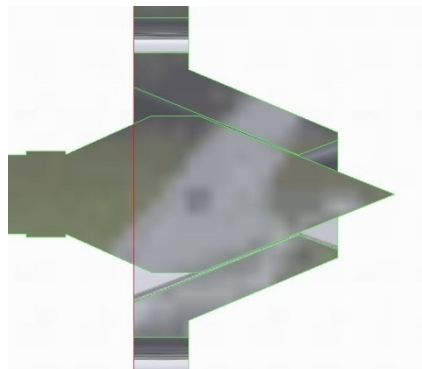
Vista seccionada de las piezas aguja y tobera en su posición cerrada.
